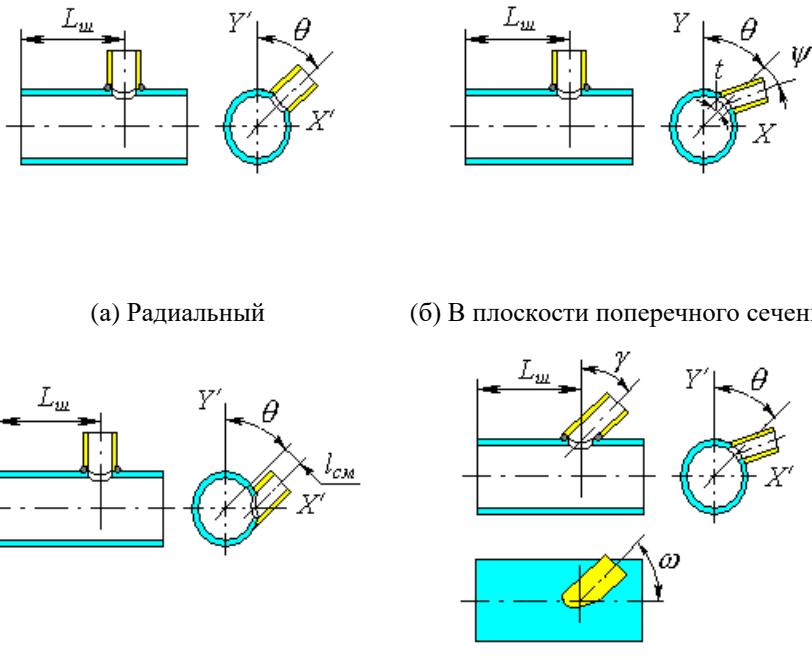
Варианты расположения штуцера на цилиндрической обечайке
